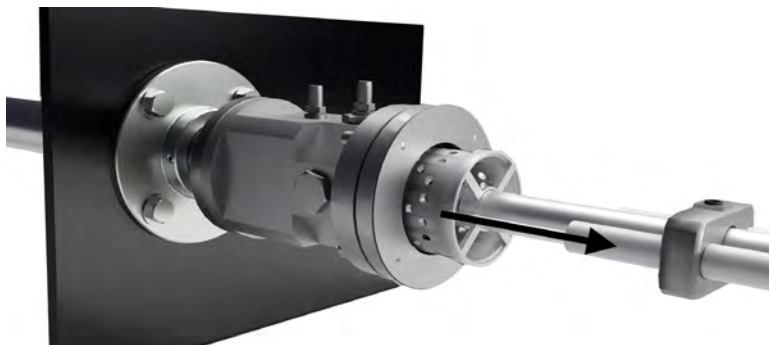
Laisser le tube extérieur et la bride traversante dans la chambre de combustion
